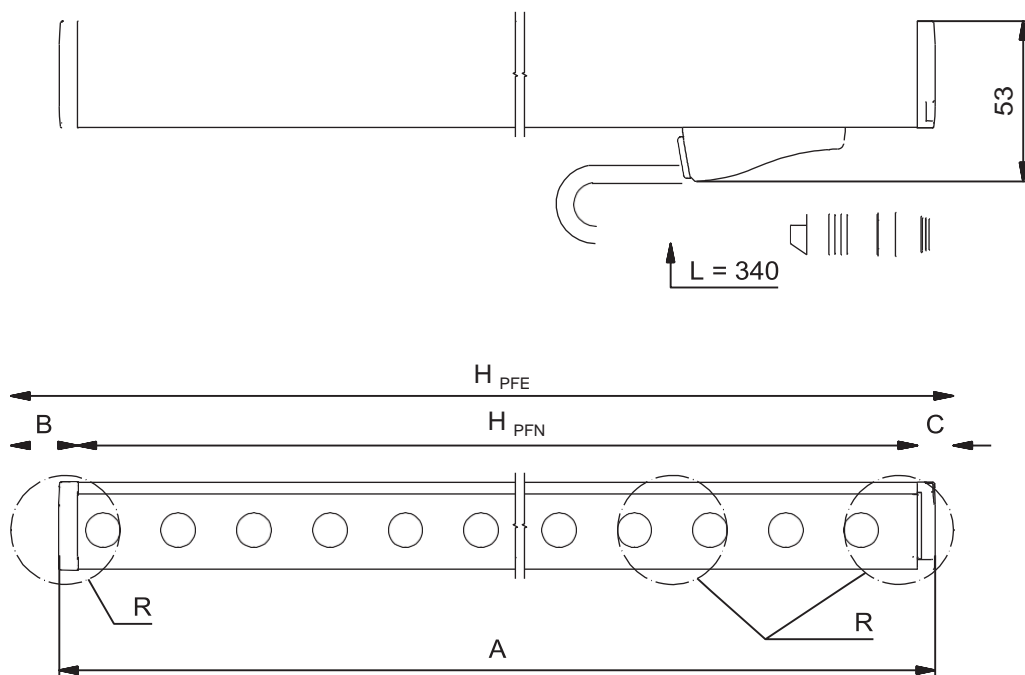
Dimensões do transmissor Guest e receptor Guest
